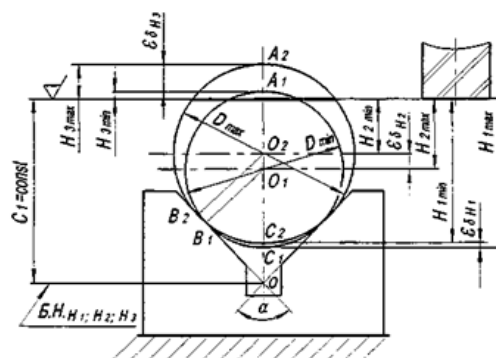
Схема настройки інструменту при фрезеруванні шпонкового пазу
